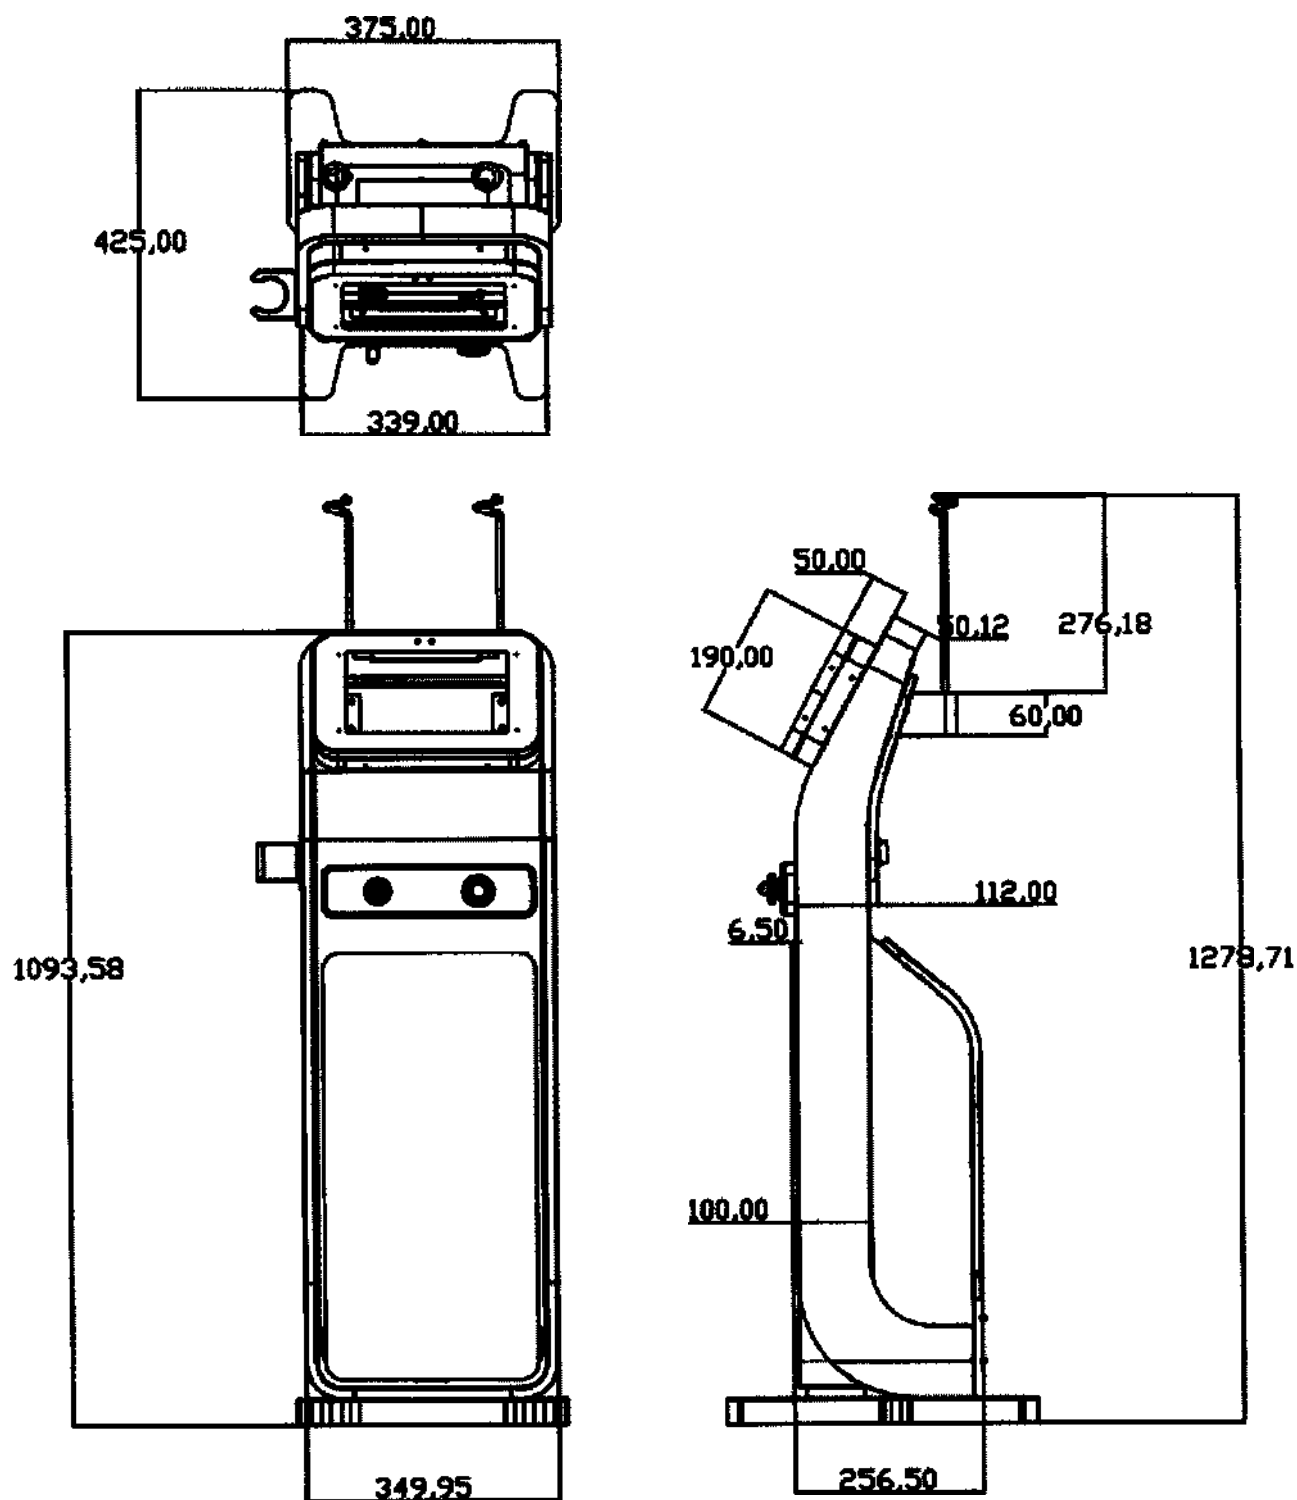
Схематический чертеж блока основного HI-REX с габаритными размерами
